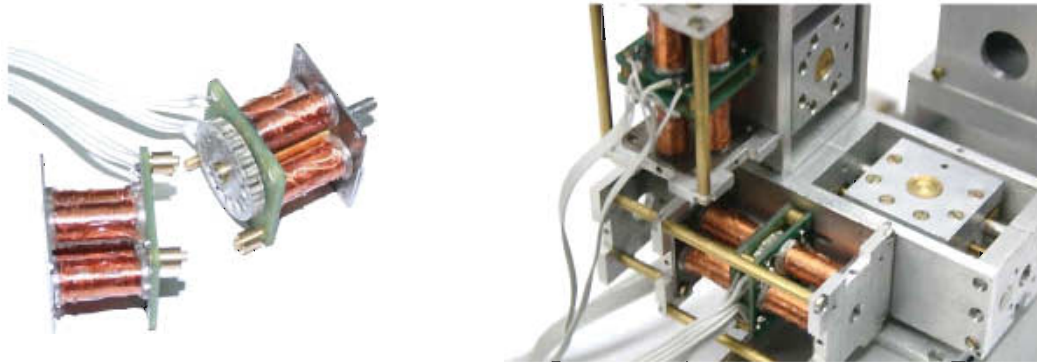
a) Motor a pasos desarrollado por el GMM. b) Motores a pasos ensamblados en la micromáquina herramienta [19].
